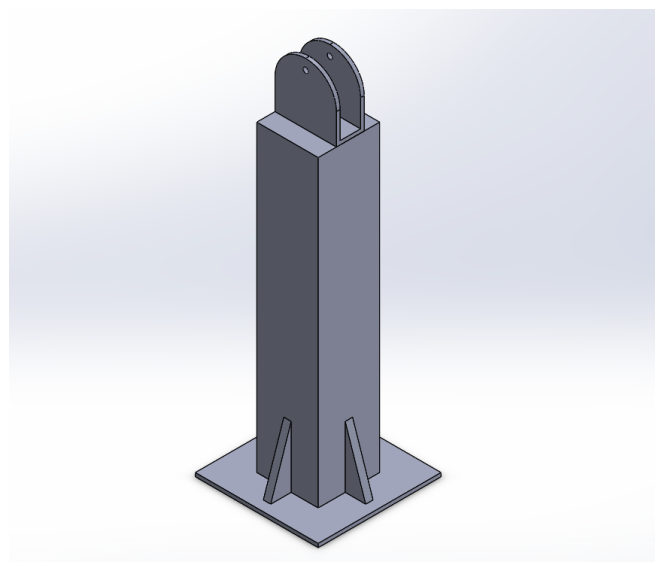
Desenho CAD da montagem do mecanismo de rotação para o primeiro grau de liberdade.
